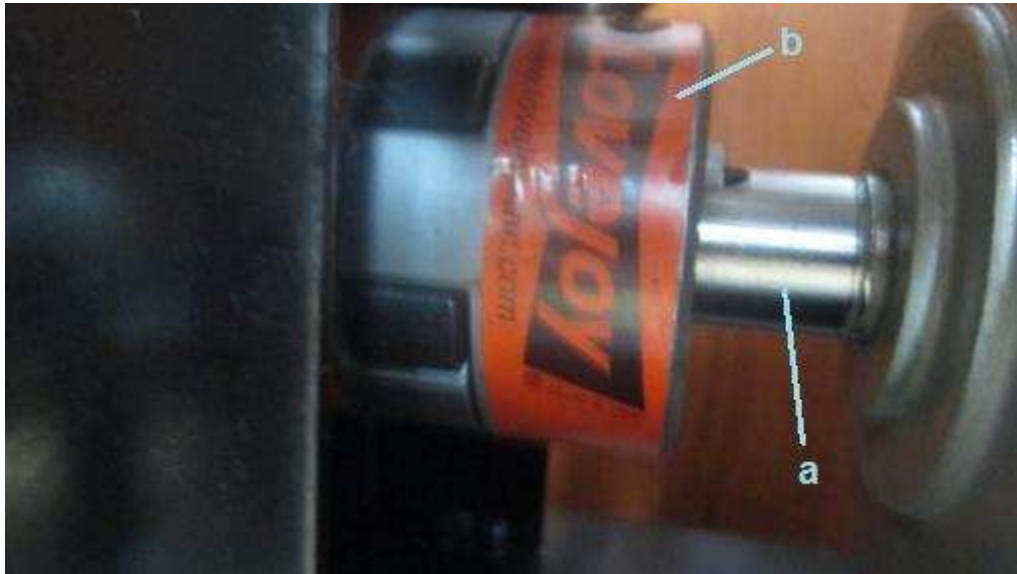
Pre-ensamble; a) Eje del motor eléctrico; b) Unión motor-bomba (marimonio)
